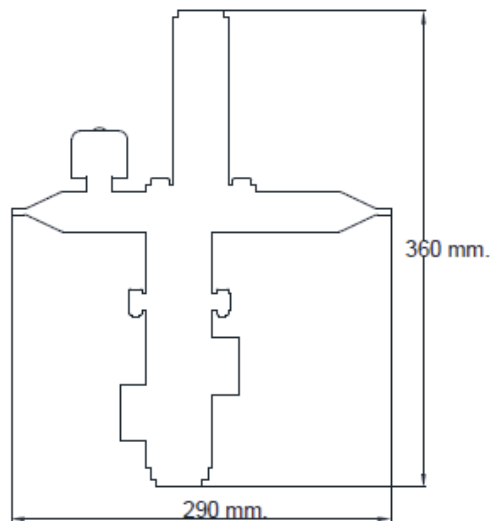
Dimensiones de Válvula de Alivio Tank Blanketing Serie 1080⁽²⁴⁾.
